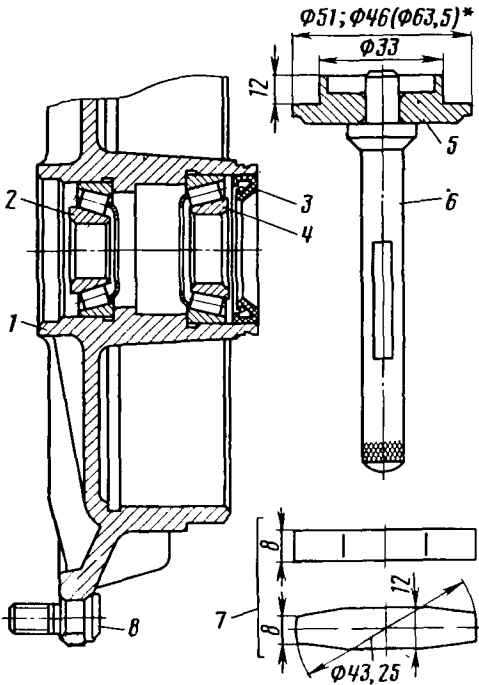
Тормозной барабан заднего колеса в сборе и оправке:
